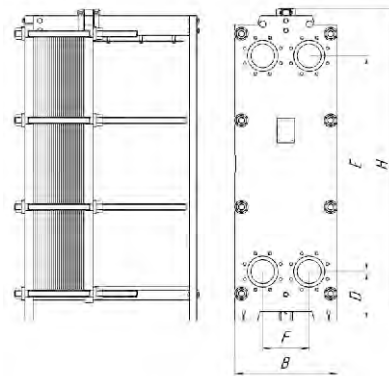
Габаритные и присоединительные размеры теплообменника пластинчатого TPx 3.
